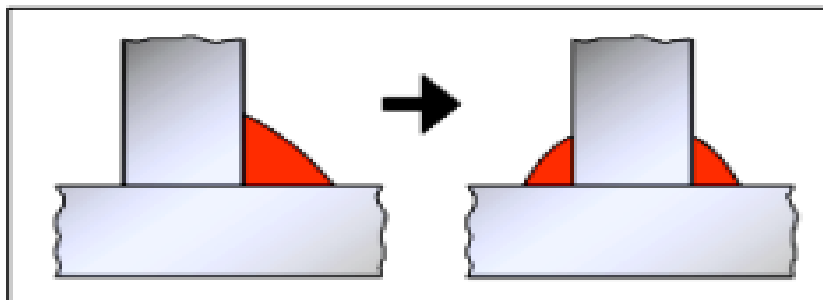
Configuration du Joint, plus petites soudures d'angle à deux faces.
